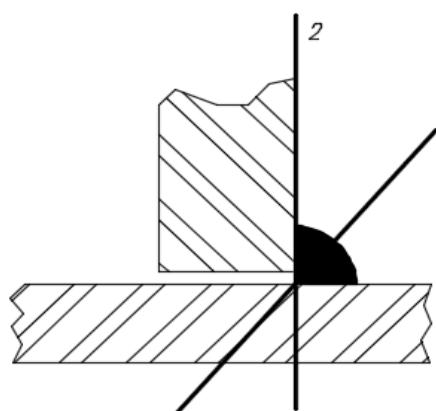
Схема расчетных сечений сварного соединения с угловым швом:
